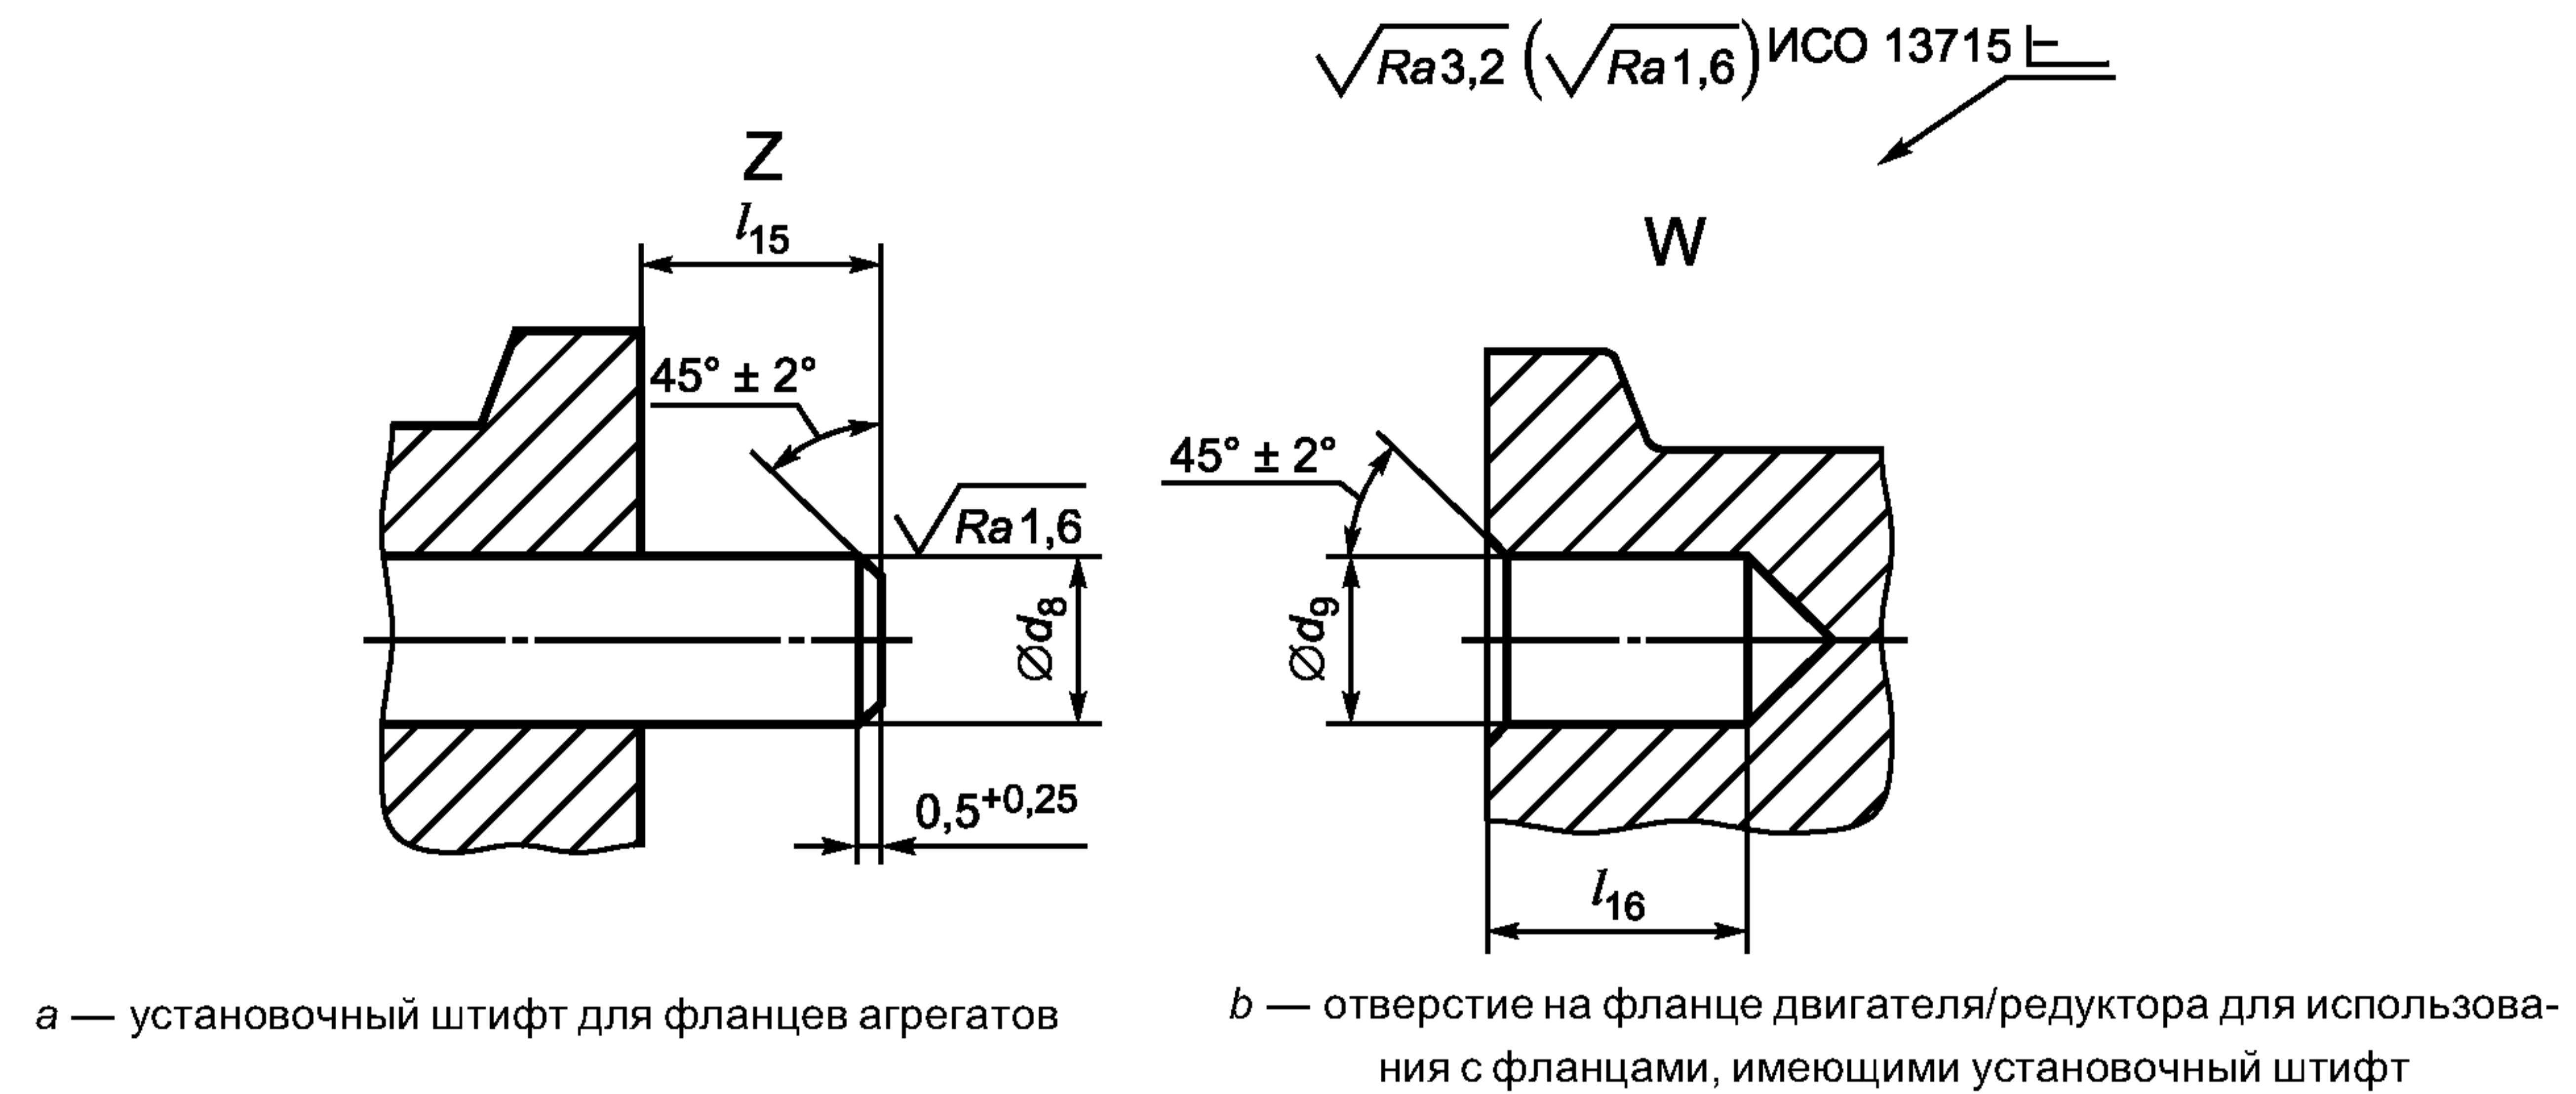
Конструкция и размеры для фланцев агрегатов и фланцев двигателя/редуктора с установочными штифтами
